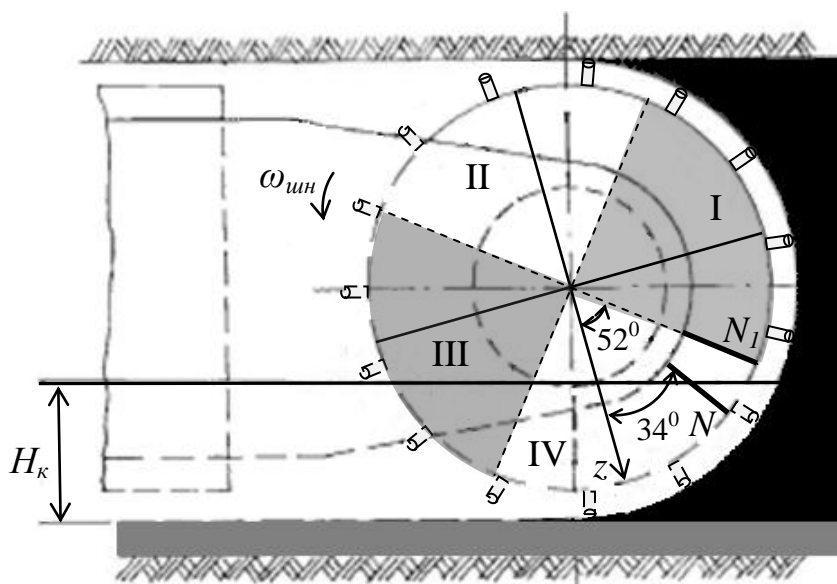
Конструктивная схема шнека (вид со стороны разгрузочного торца)
